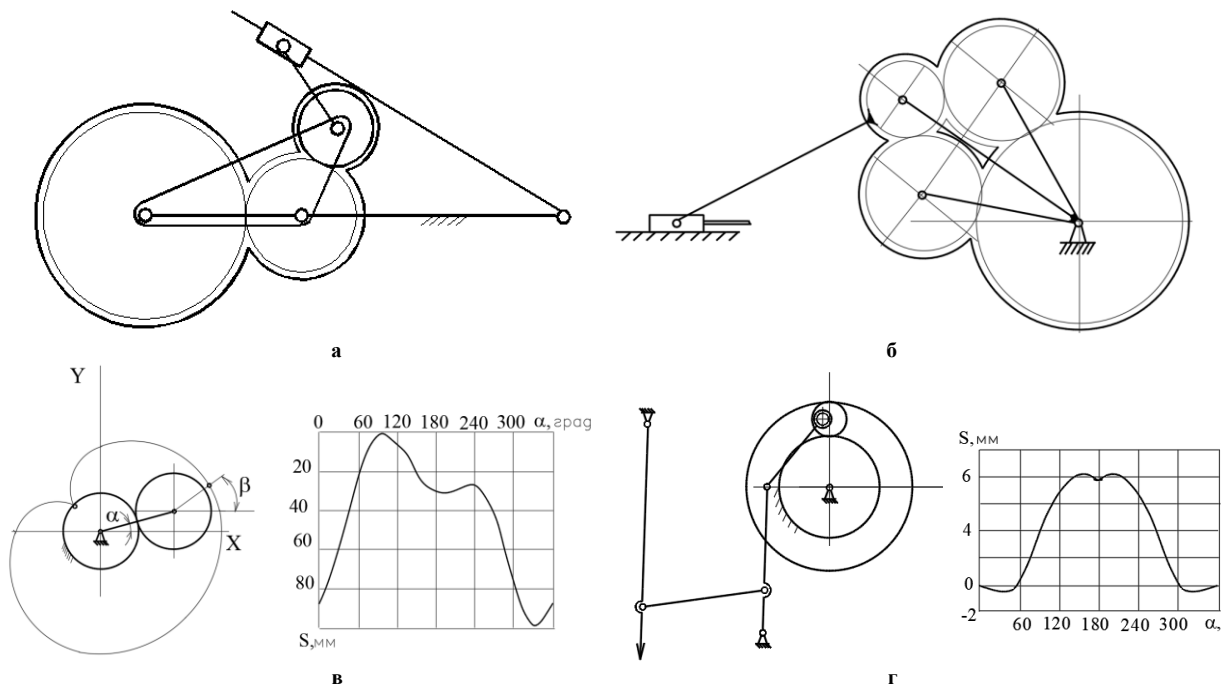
Зубчато-важільні механізми: а - механізм з коливальним рухом вихідної ланки; б - механізм приводу рапір ткацького станка типу АТПР; в - планетарний механізм ниткопритягувача швейної машини; г - планетарний механізм відхилення рамки швейної машини
